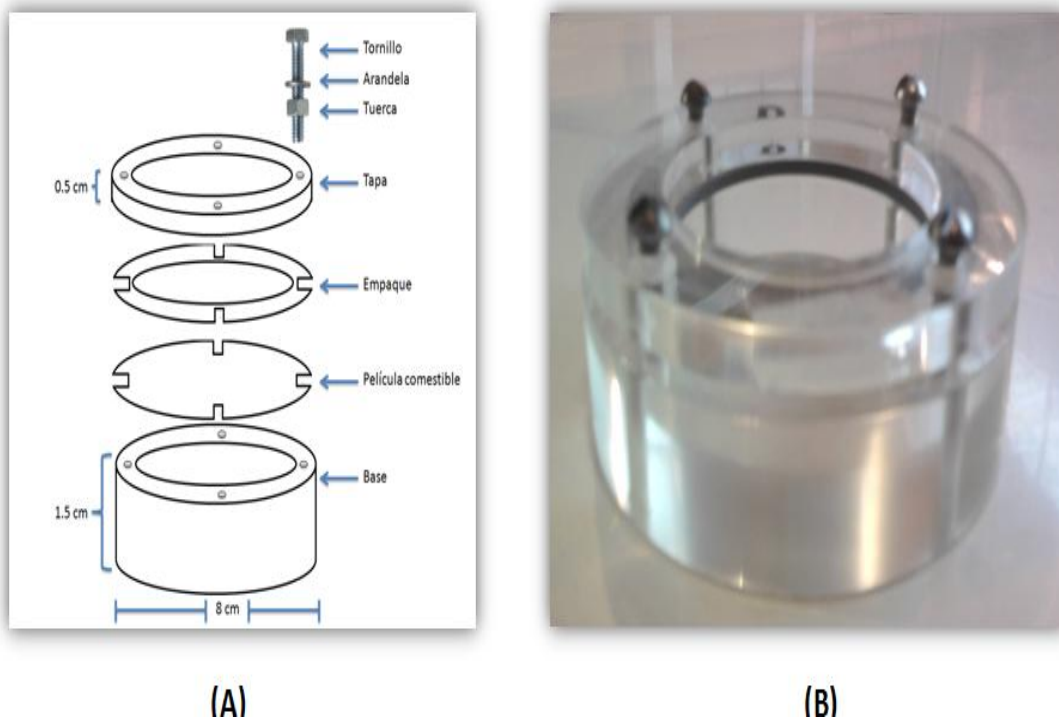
(A) Esquema de ensamble y dimensiones de la celda utilizada, (B) Ensamble completo de la celda para medir permeabilidad al vapor de agua.
